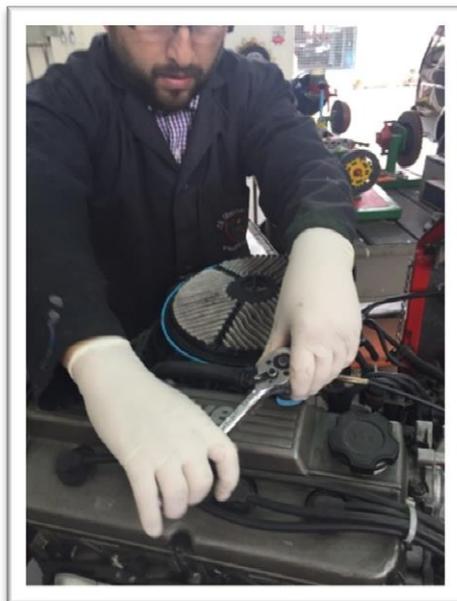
Instalación filtro de aire / Fuente: Propia del autor
